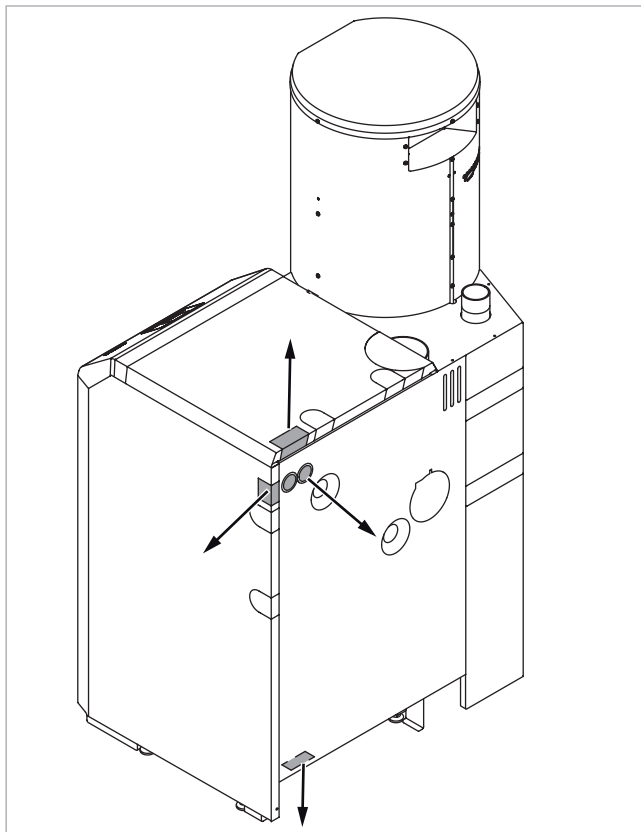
Kabeldurchführungen – Ansicht von hinten
